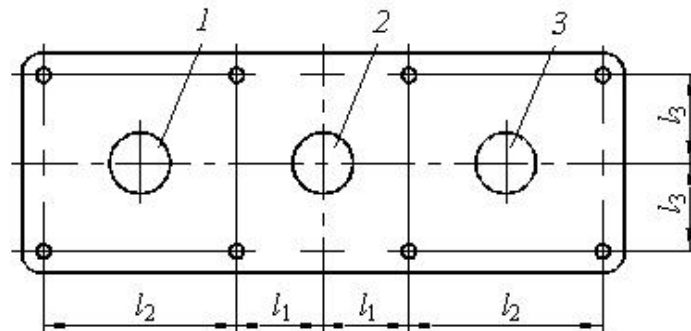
Схема расположения резьбовых соединений гидроблока к корпусу механической части насоса
